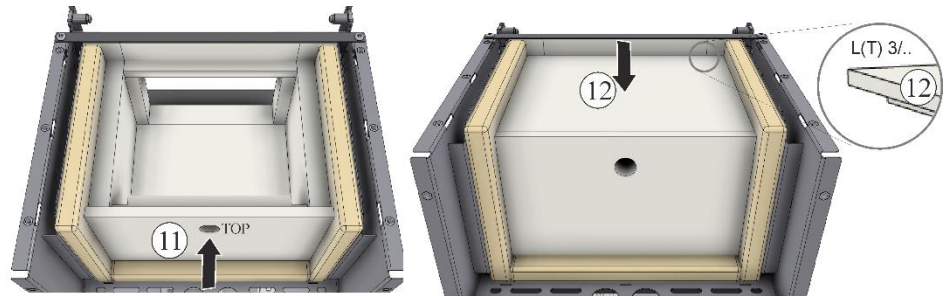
Colocación del aislamiento de la pared posterior y del techo (figura análoga)
